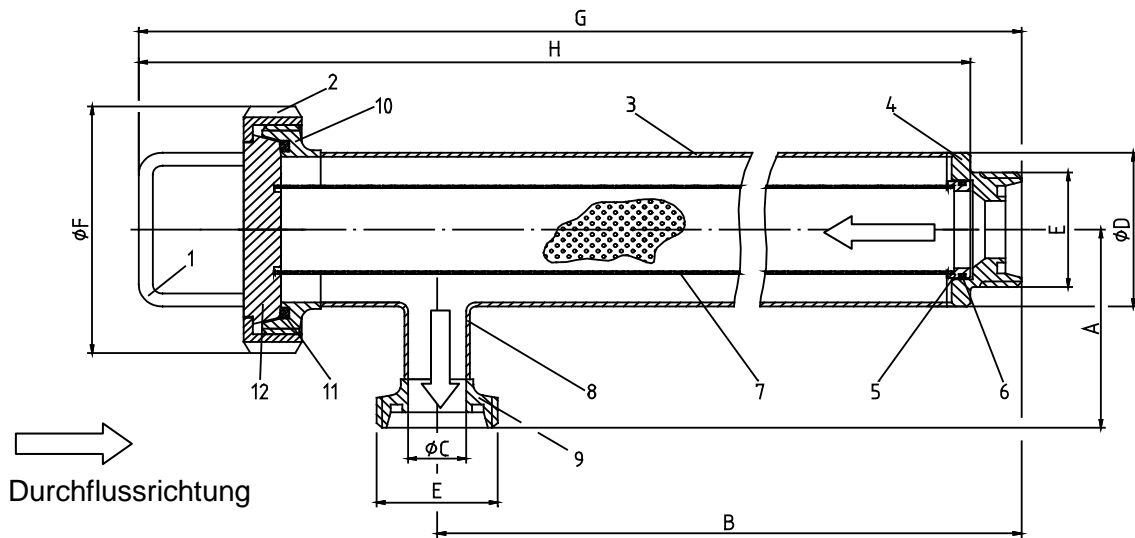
Schnitt Eckrohrsieb GG Standardausführung (Abmessungen siehe Kapitel 10.1)
